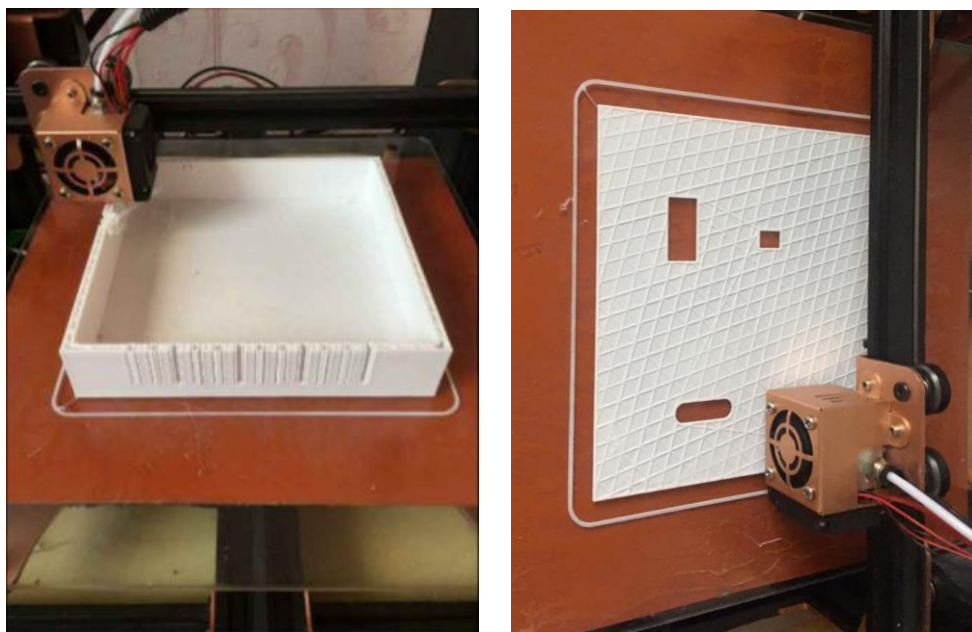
Процесс изготовления 3D-модели корпуса для разработанного устройства
